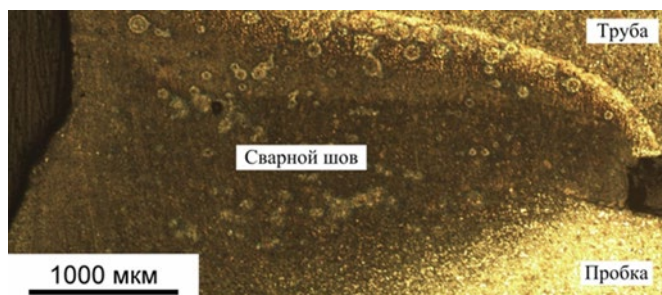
Макроструктура сварного соединения [14]
